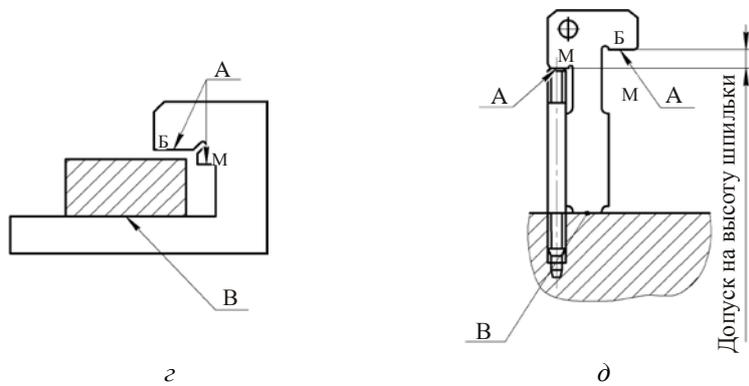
Примеры контроля глубин и высот уступов калибрами методом «надвигания» с расположением полей допусков по схеме 1 (см. рис. 2.14):
